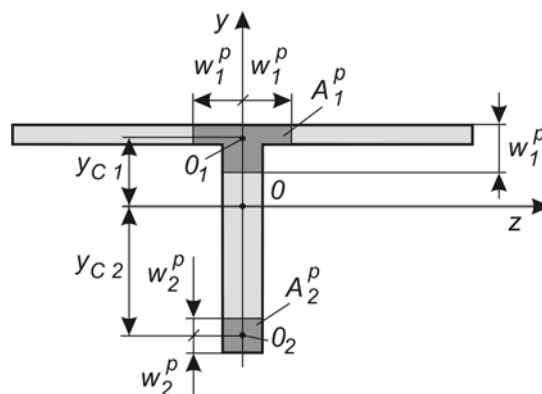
Зона пластических деформаций поперечного сечения сварной балки.
